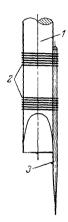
Приспособление для пробивания отверстий в пластинах из оргапического стекла.
